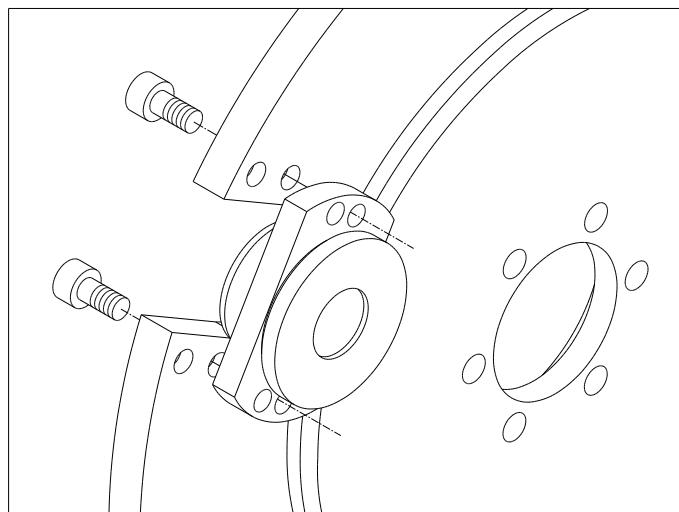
Сборка фланцевого планетарного держателя-фланцевого планетарного диска
